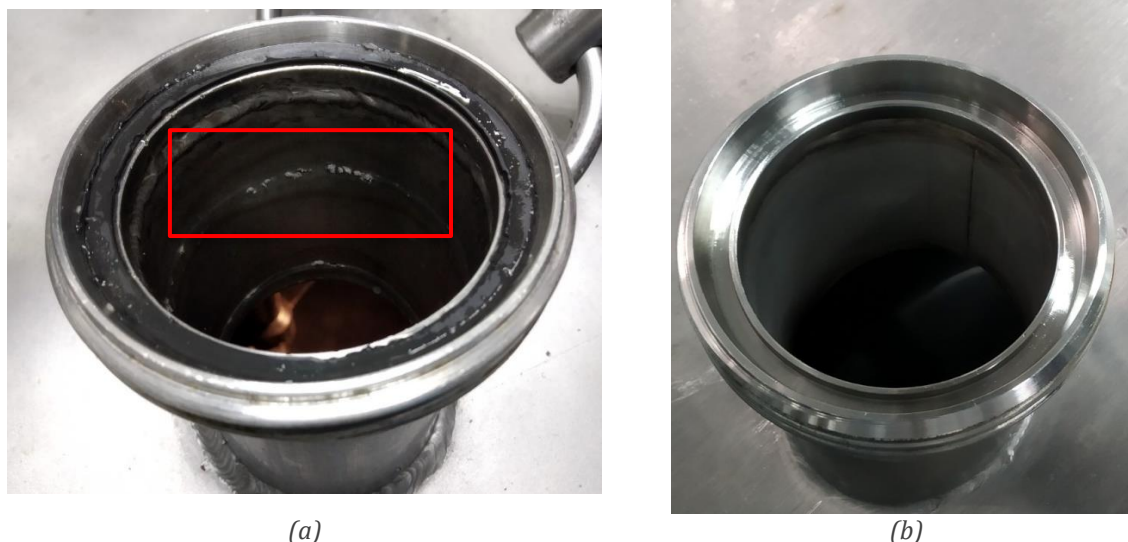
Boca del tanc DM33 amb punts de soldadura (a) i el tanc DM31 llis (b)
